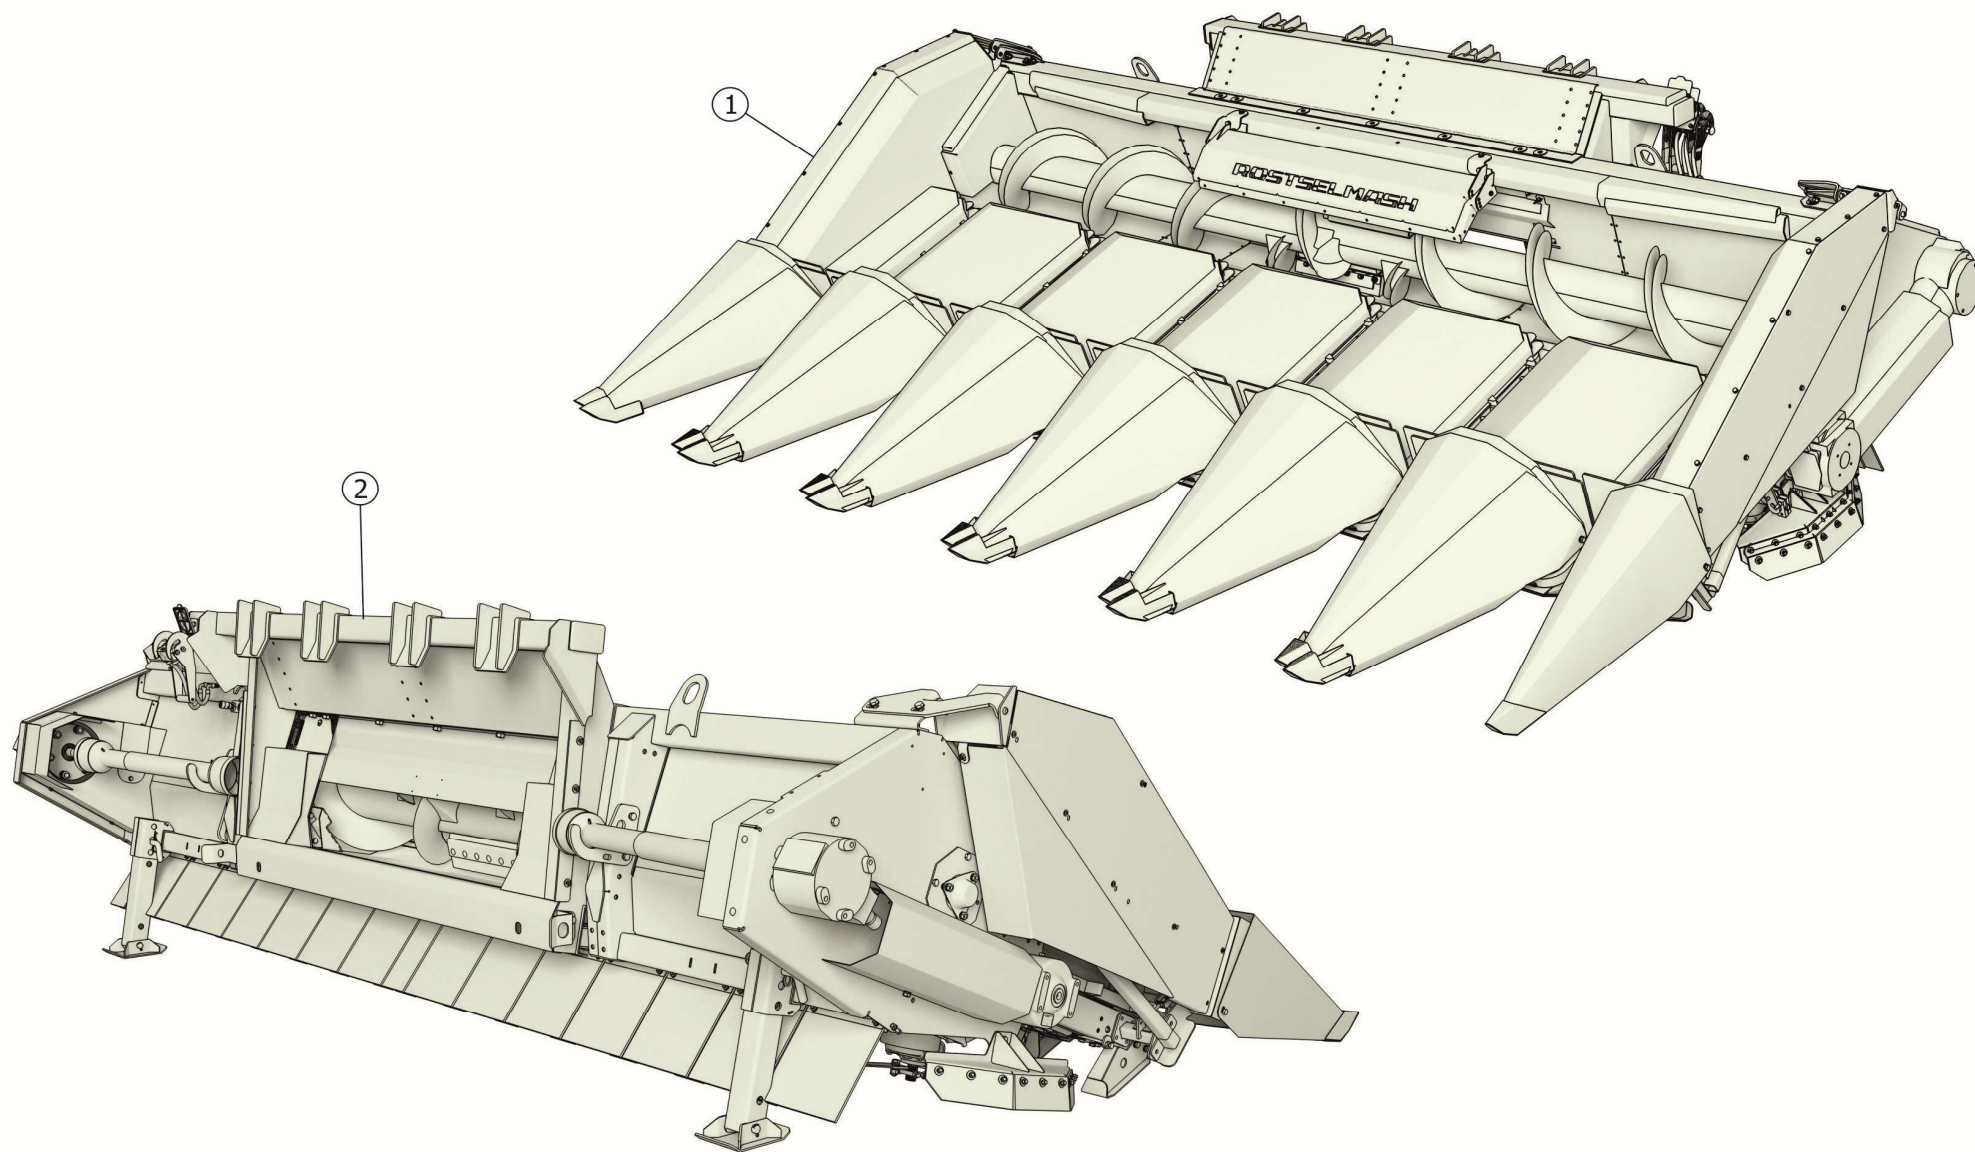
Приспособление для уборки кукурузы ППК-61-75 ЕРР
